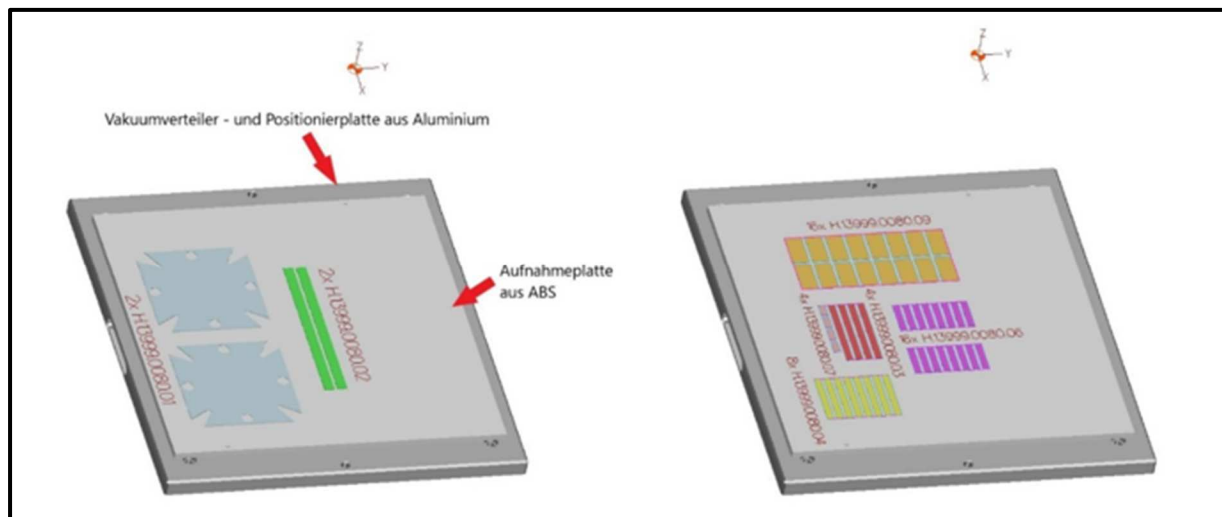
Flachteilaufnahmen für Fräsbeschnitt von Prüfkörper / 29.06.23 Lakowa intern
